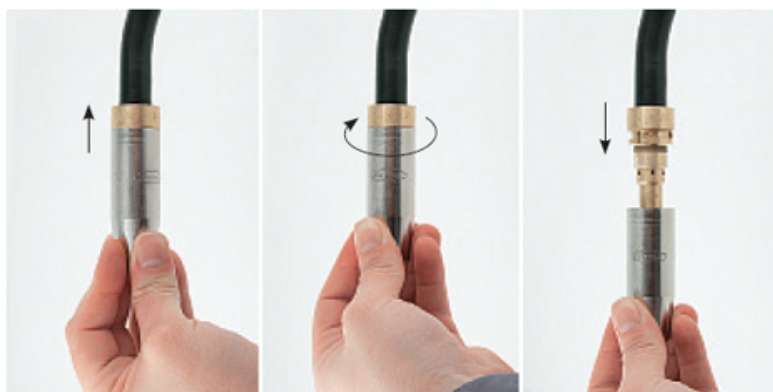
Способ закрепления газового сопла Quick Snap фирмы Fronius
